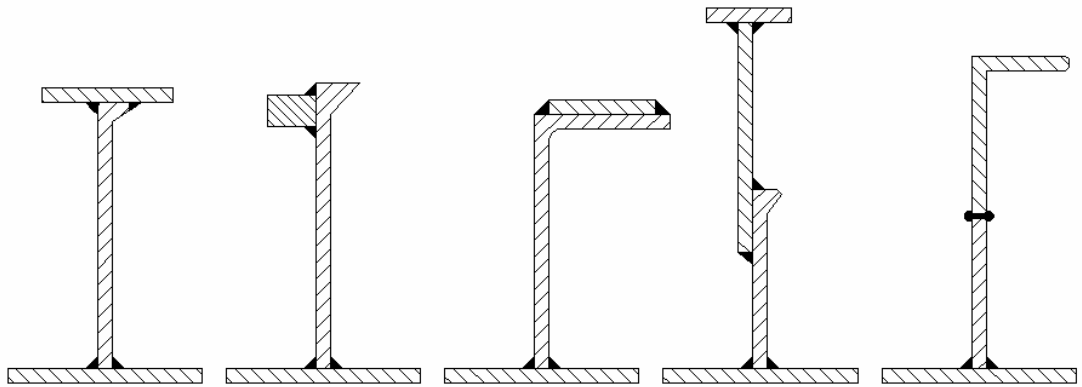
Схема подкрепления штатного набора бортового перекрытия
